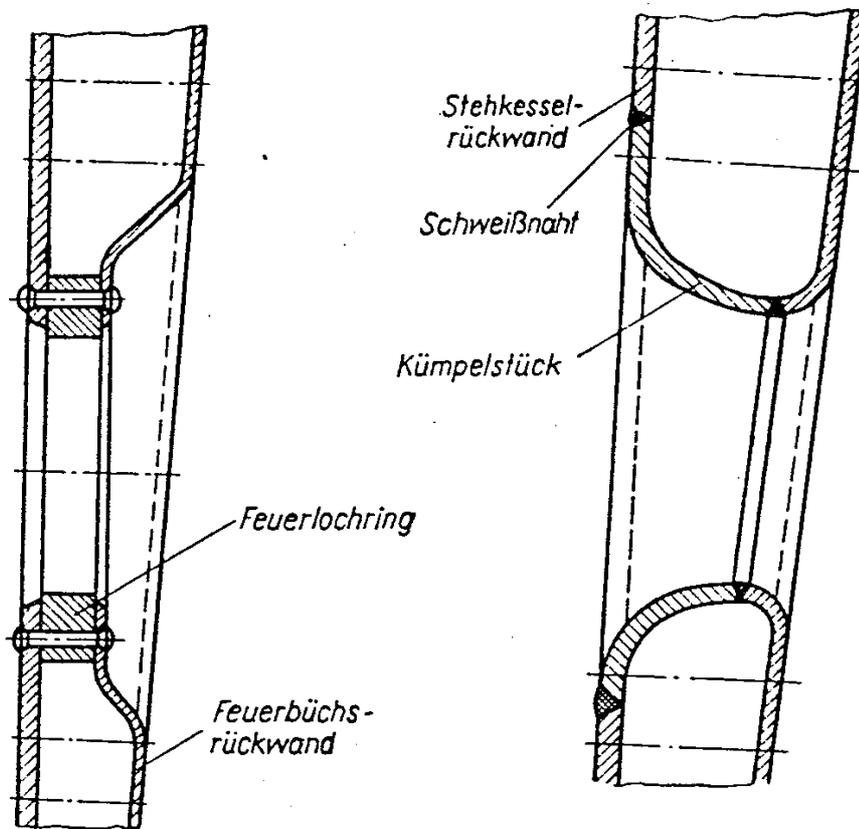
Feuerlochring am genieteten und geschweißten Kessel
